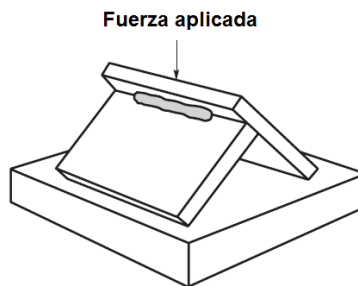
Prueba de fractura en una probeta soldada en "T"
